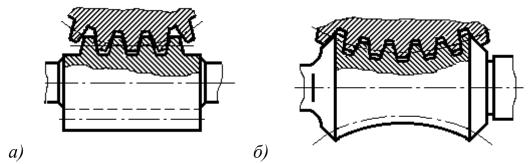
Формы поверхности для нарезки резьбы: a – цилиндрическая,  $\delta$  – глобоидная
